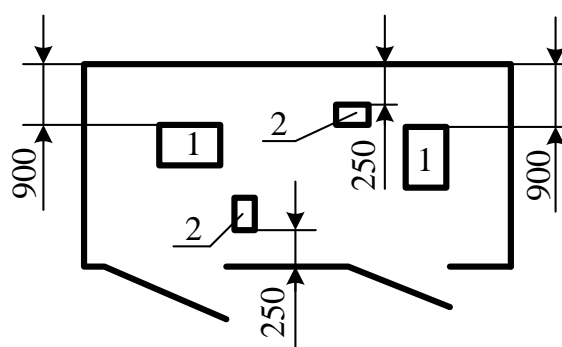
Схемы расположения сварочного оборудования для постовой сварки:
